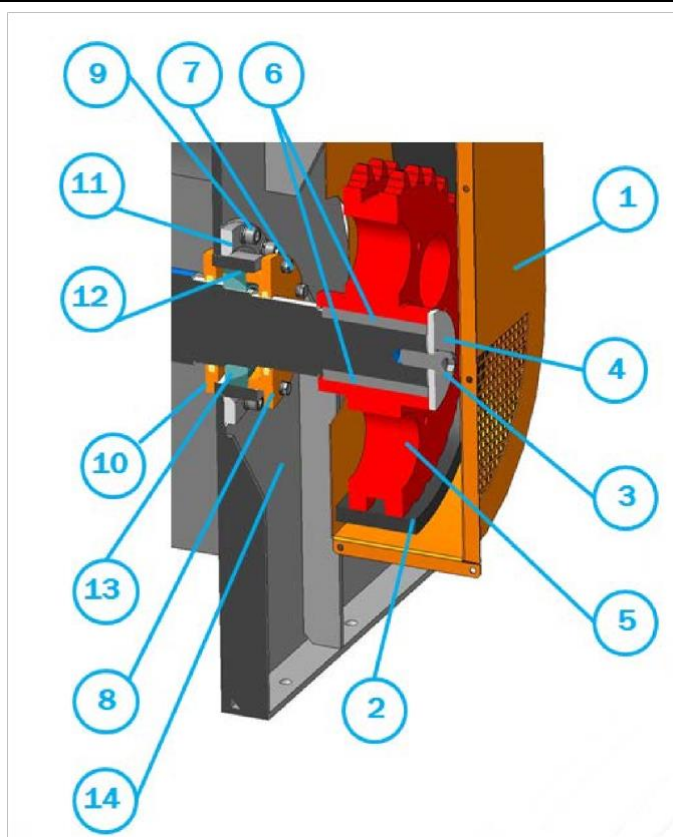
Схема демонтажа подшипника передней опоры.
